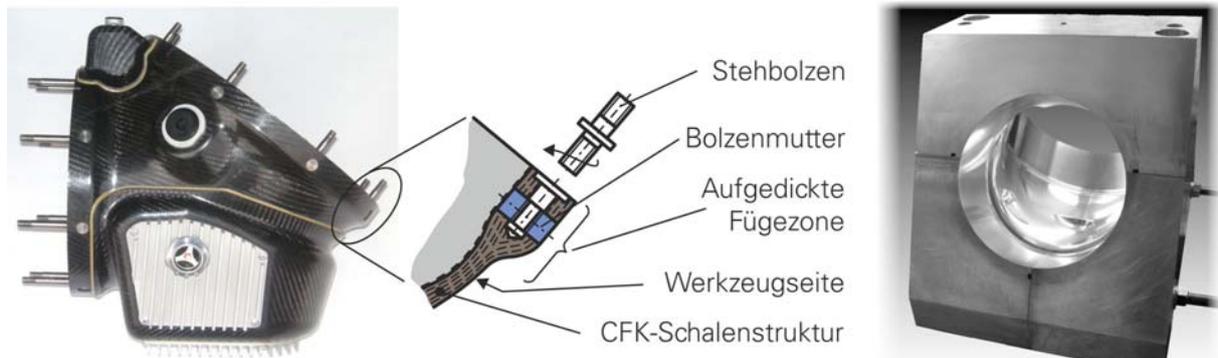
Gehäusestruktur für ein Hubschrauber-Getriebe, gefertigt mittels Prepreg-Autoklav-Technik (links); Anpassung von Laminatstärken in den Fügezonen (Mitte); dreiteiliges Laminierwerkzeug aus Aluminium für die Urformung der Hauptstruktur (rechts)
